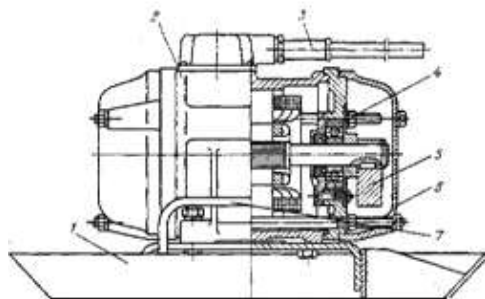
Схемы оборудования для поверхностного уплотнения бетонных смесей
